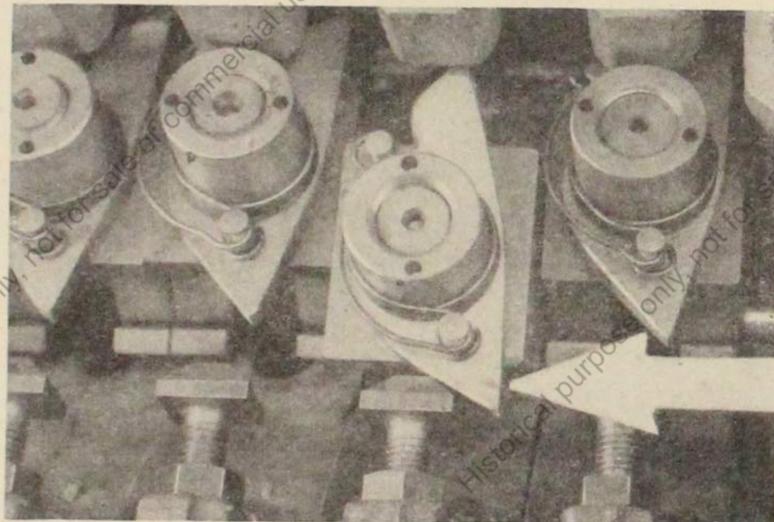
Nachstellvorrichtung ist übergekippt, Anschlagplatte wird durch die Pyramidenschraube gedreht
